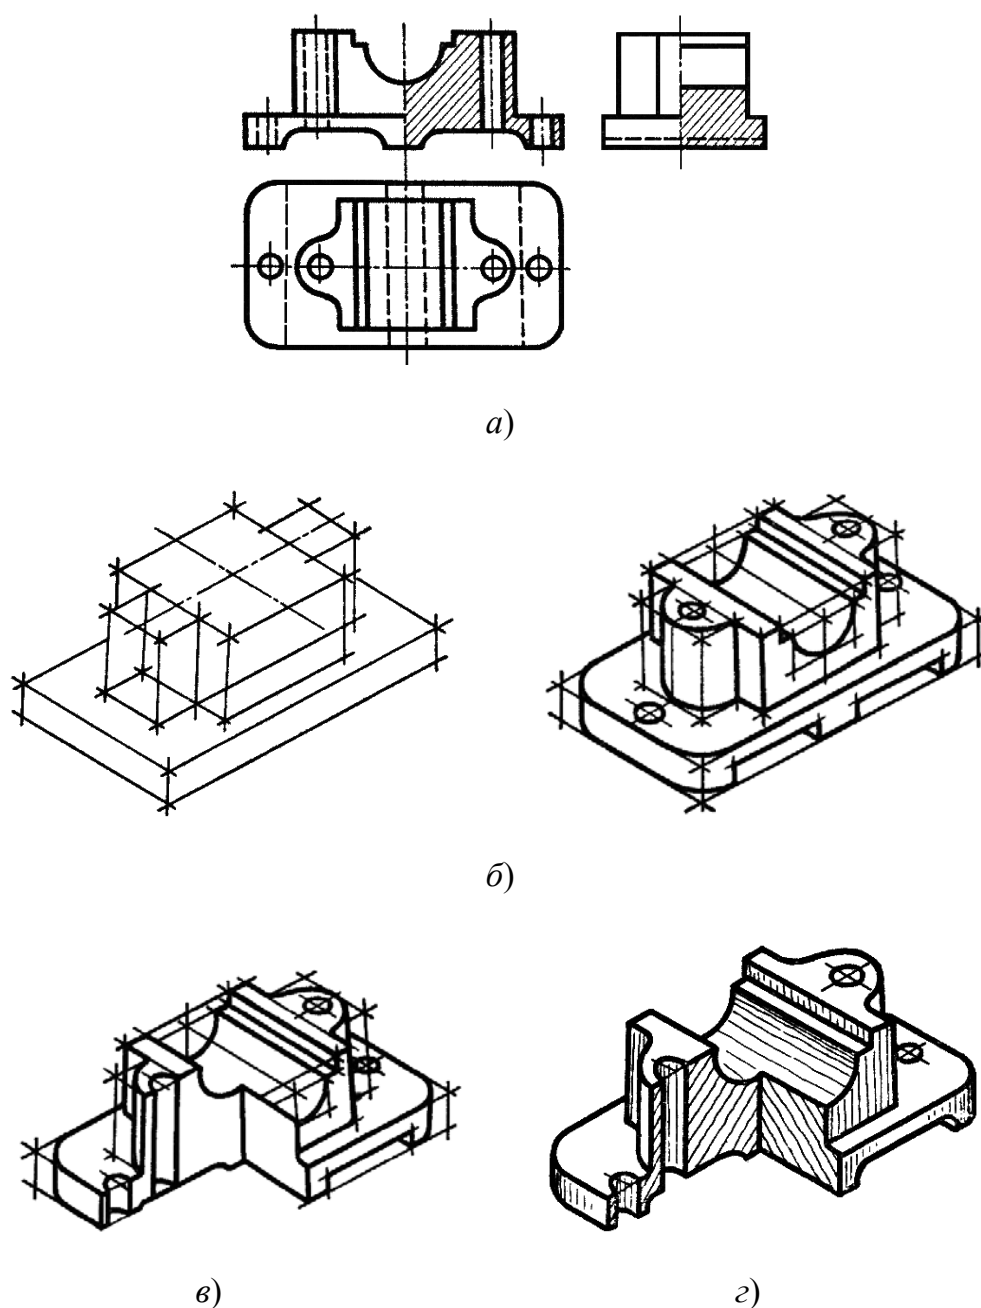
Порядок выполнения рисунка корпуса подшипника
